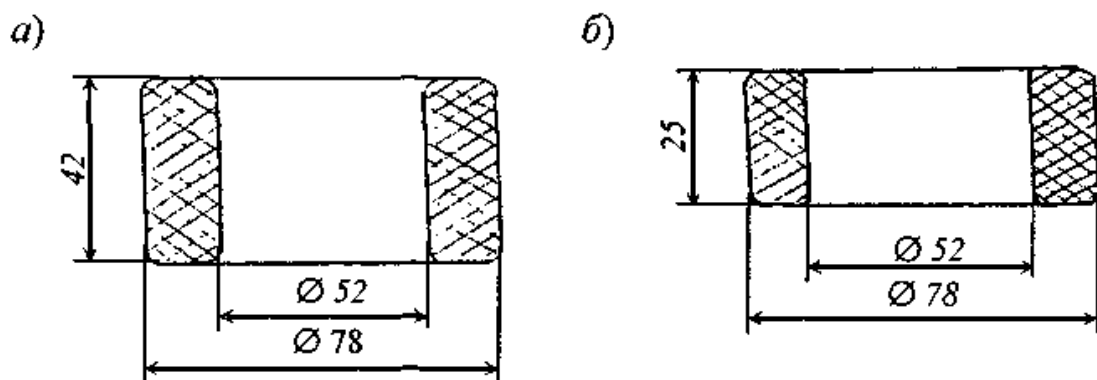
Гумові втулки-заготовки до запресування:
